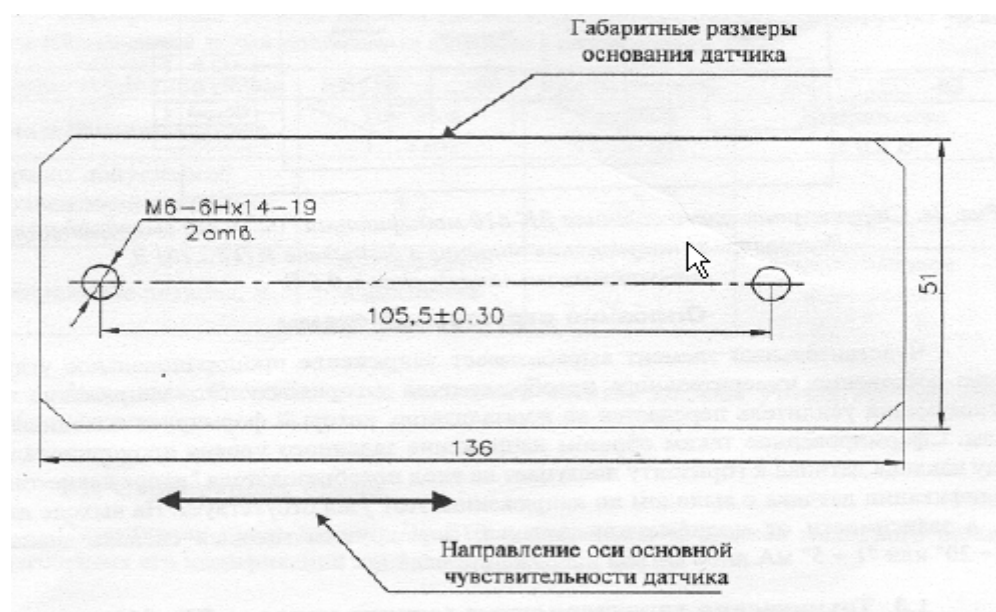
Разметка под установку датчика-преобразователя ТМК-163
